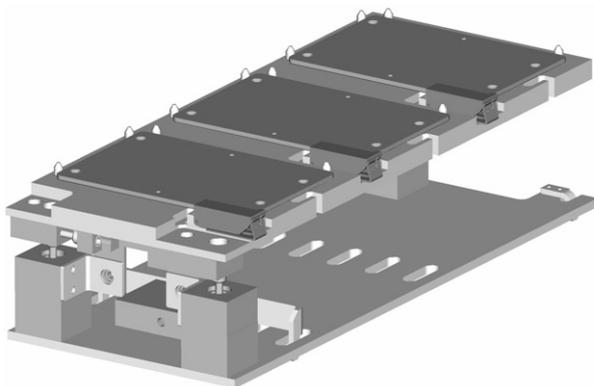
Träger für 3 1536-Well-Mikrotiterplatten, quer ausgerichtet
